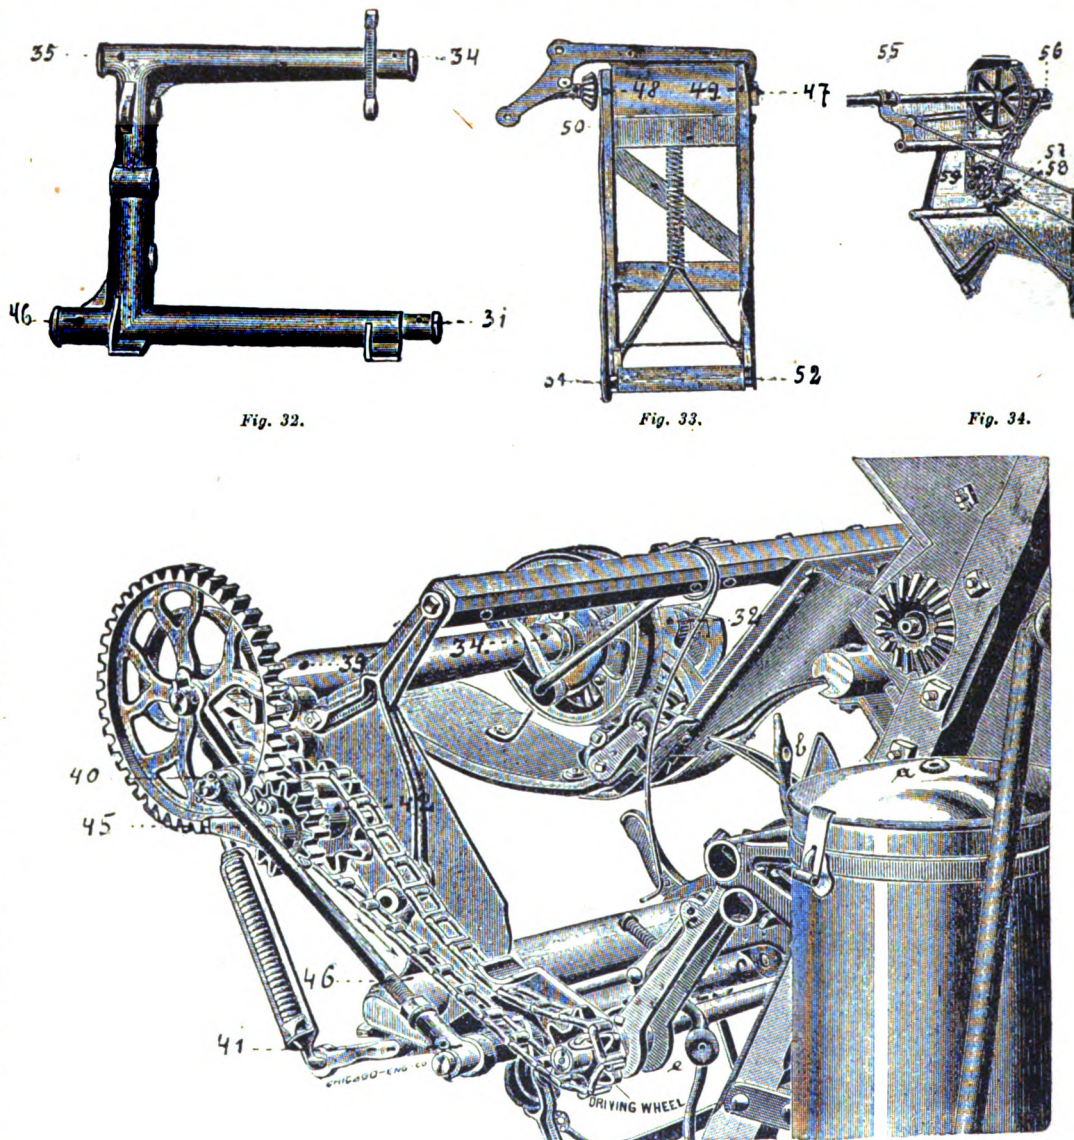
35. Einzeltheile der Mähmaschine von der Mc. Cormick Harvesting Machine Co., Chicago.
